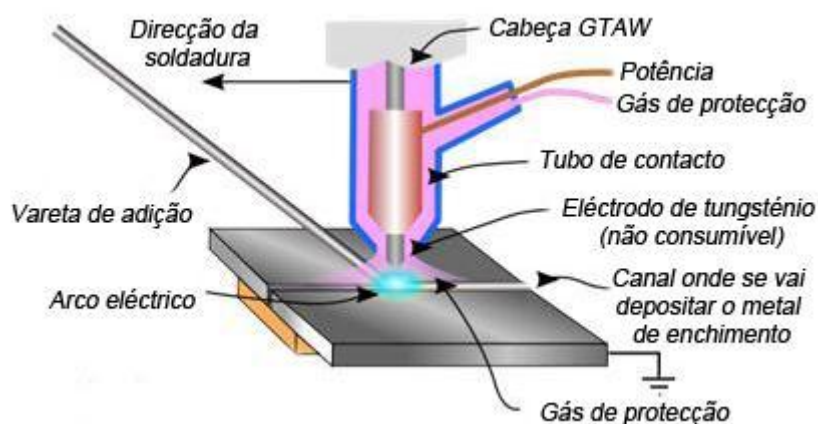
Esquema do processo de soldadura TIG [15]
